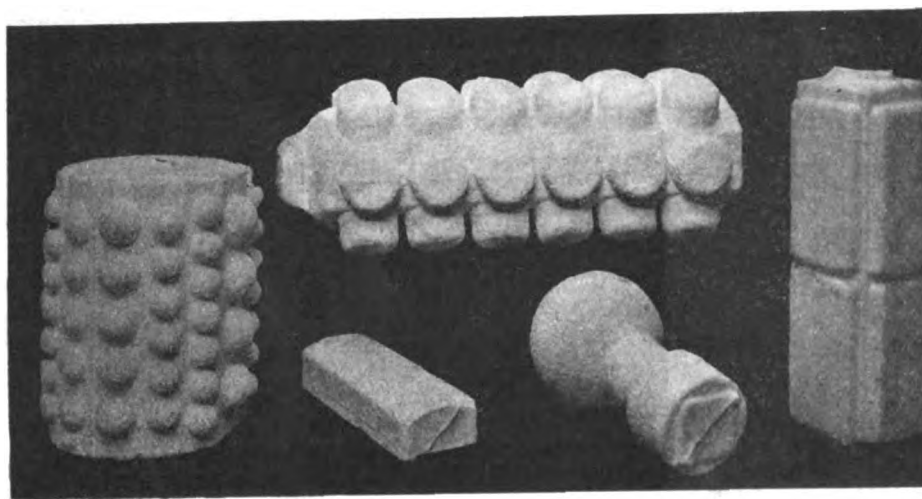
Vue de quelques pièces brutes de silice fondu après le moulage et avant le découpage.
